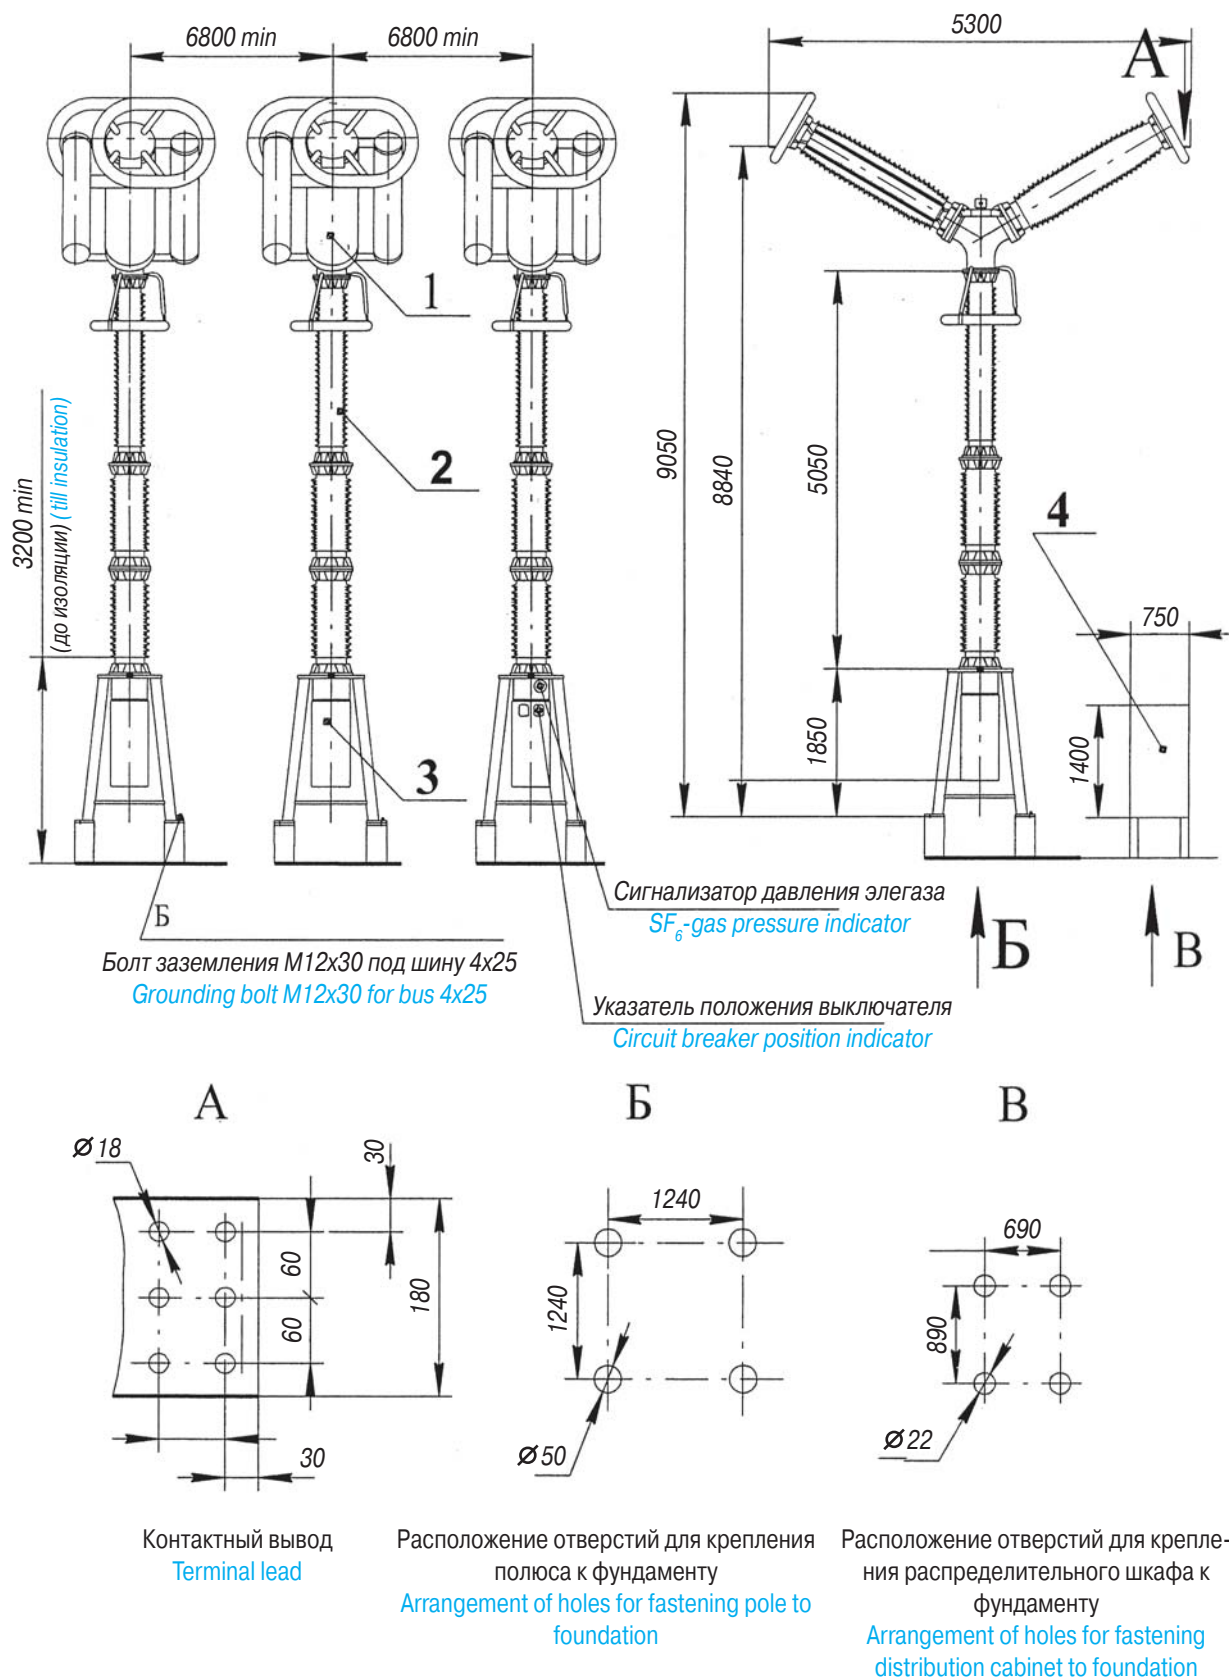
Габаритные, установочные и присоединительные размеры выключателя ВГК-500
